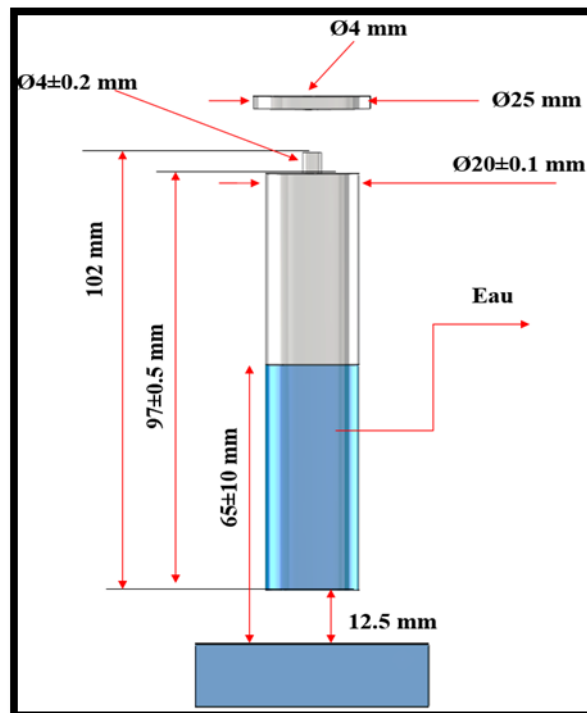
Dessin et dimensions de l'éprouvette de trempabilité en bout (Jominy).
